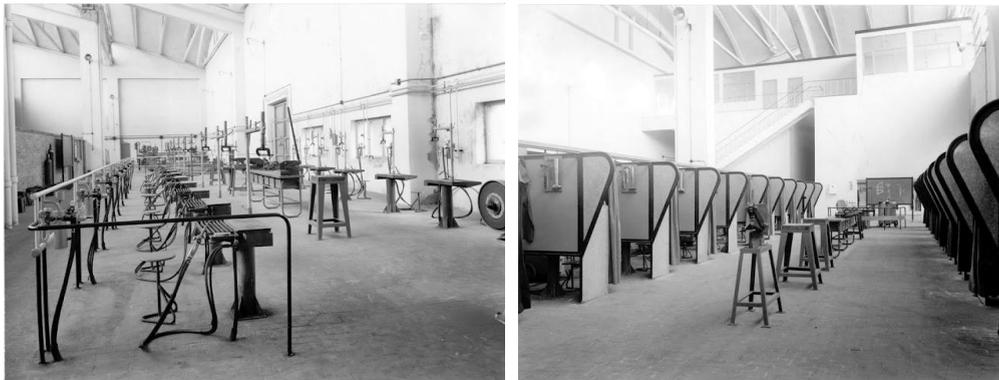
a | b. Taller de soldadura con las zonas de soldadura oxiacetilénica y la zona de cabinas para soldadura eléctrica.
